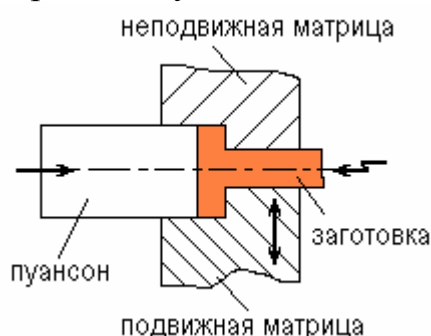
Схема штамповки на горизонтально-ковочной машине
